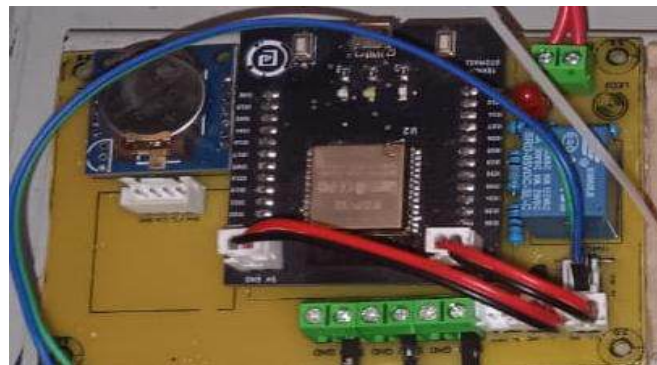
Routing Board Bottom PCB (Extension ESP32)
